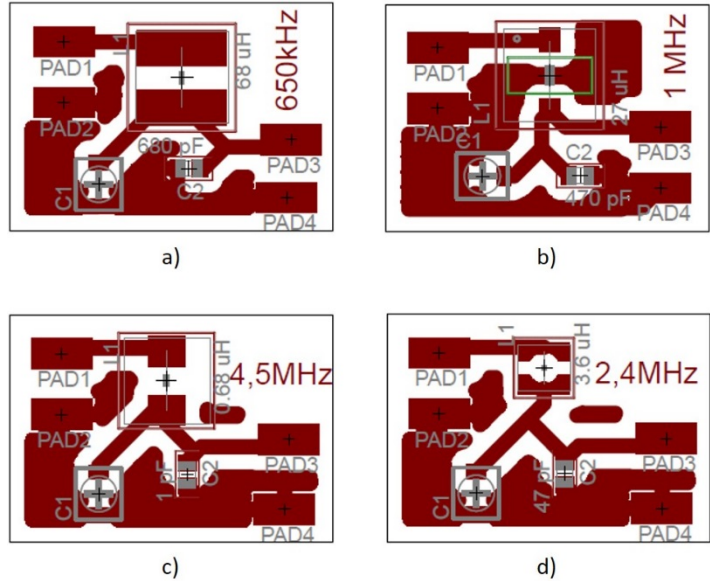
Board dei circuiti di matching realizzate con CAD EAGLE.
